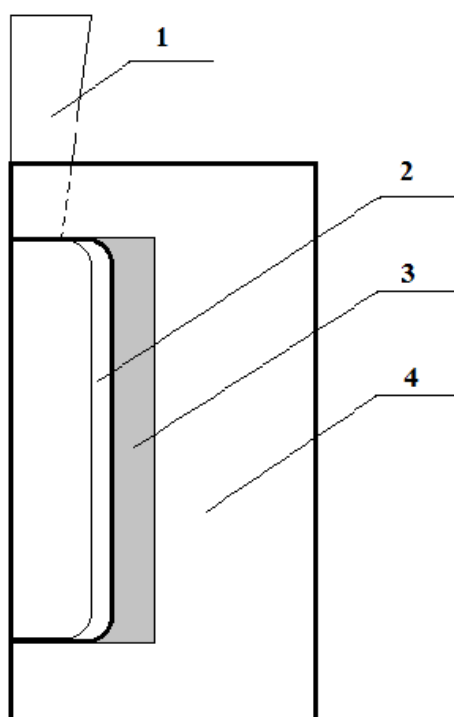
Устройство для изучения кинетики набора керамических заготовок:
